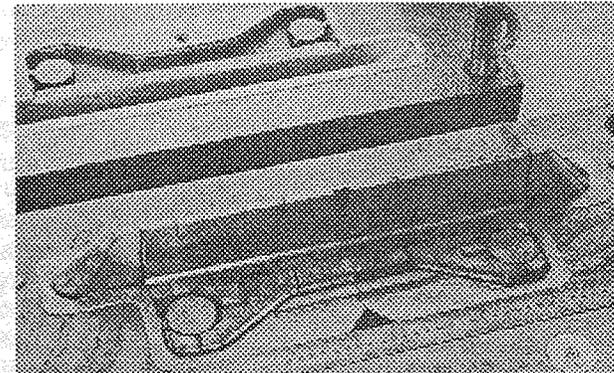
Durch Selected Laser Sintering von Metallpulver erzeugter Formeinsatz
